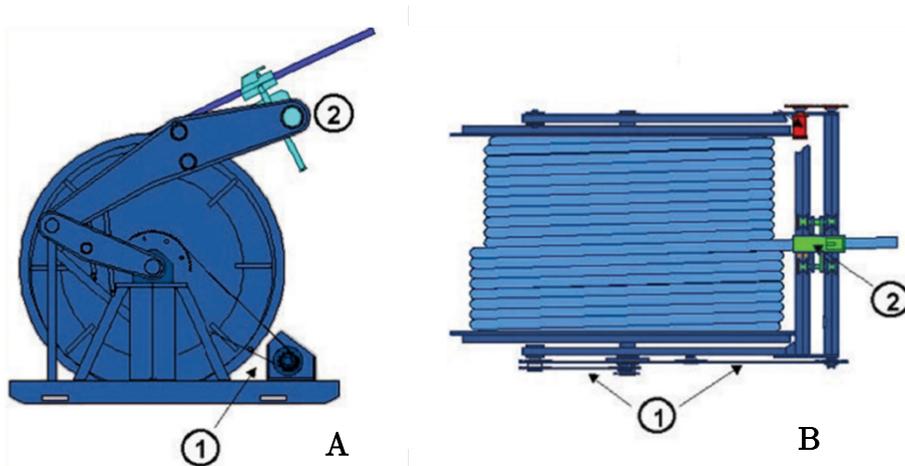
La bobine de Coiled Tubing. A. bobine de CT vue de face. B. bobine de CT vue de dessus. (1. système d'entraînement de bobine. 2. Assemblage de nivellement).
